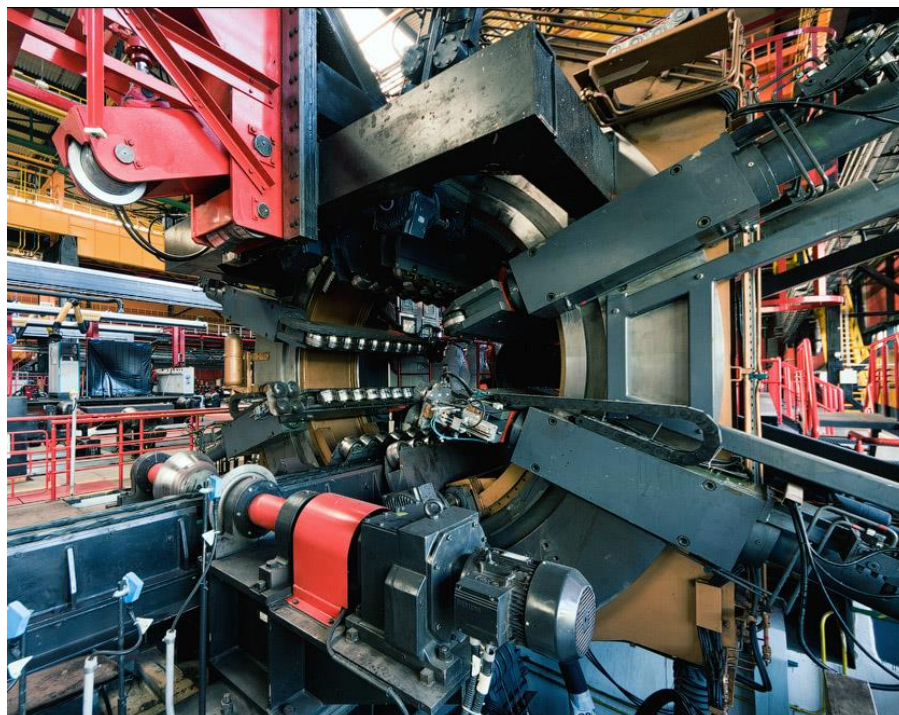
Клеть сборочно-сварочного стана
